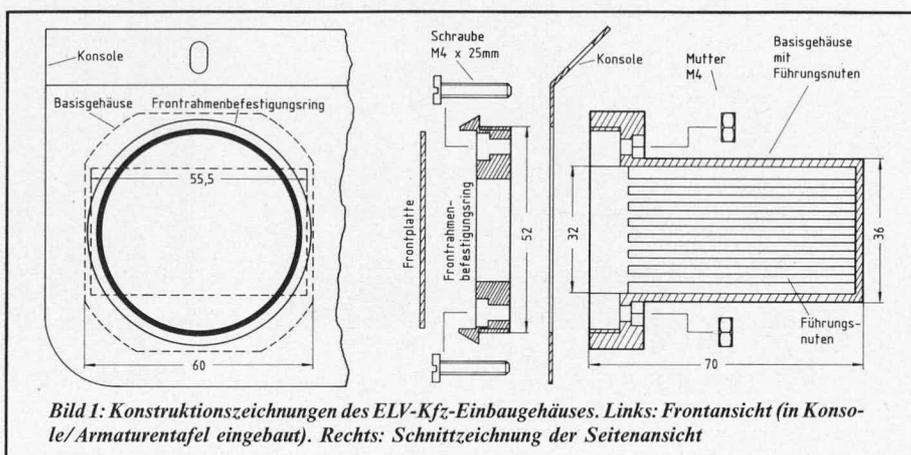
Konstruktionszeichnungen des ELV-Kfz-Einbaugehäuses. Links: Frontansicht (in Konsole/Armaturentafel eingebaut). Rechts: Schnittzeichnung der Seitenansicht
